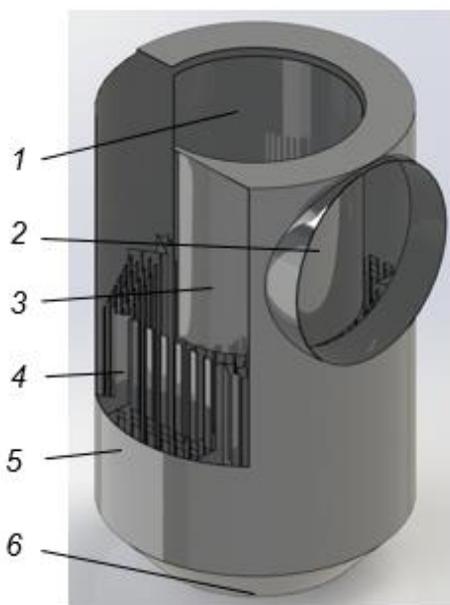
3D модель устройства: 1 – патрубок для подвода газа; 2 – патрубок для отвода очищенного газа; 3 – выпускная труба; 4 – ряды двугавровых элементов; 5 – корпус сепарационного устройства; 6 – дополнительный выходной патрубок для отвода уловленных частиц пыли
